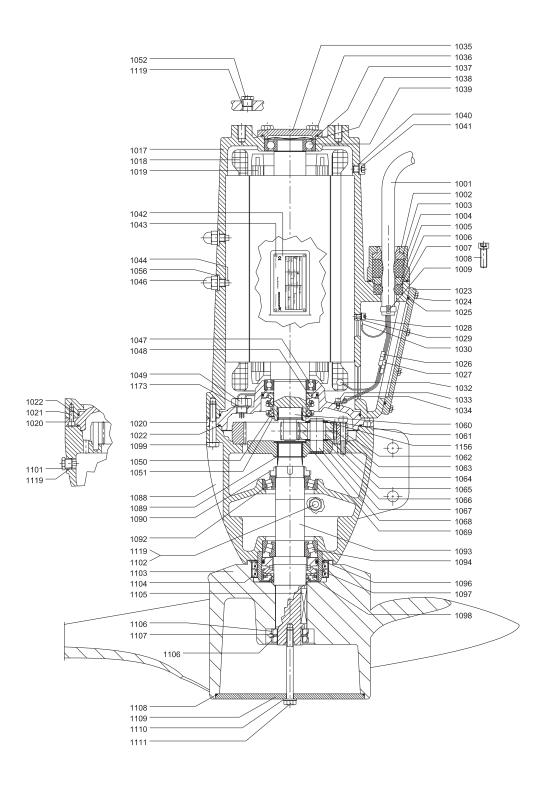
Чертёж в разрезе, SRP.70.80.xxx, SRP.100.80.xxx и SRP.130.80.xxx
